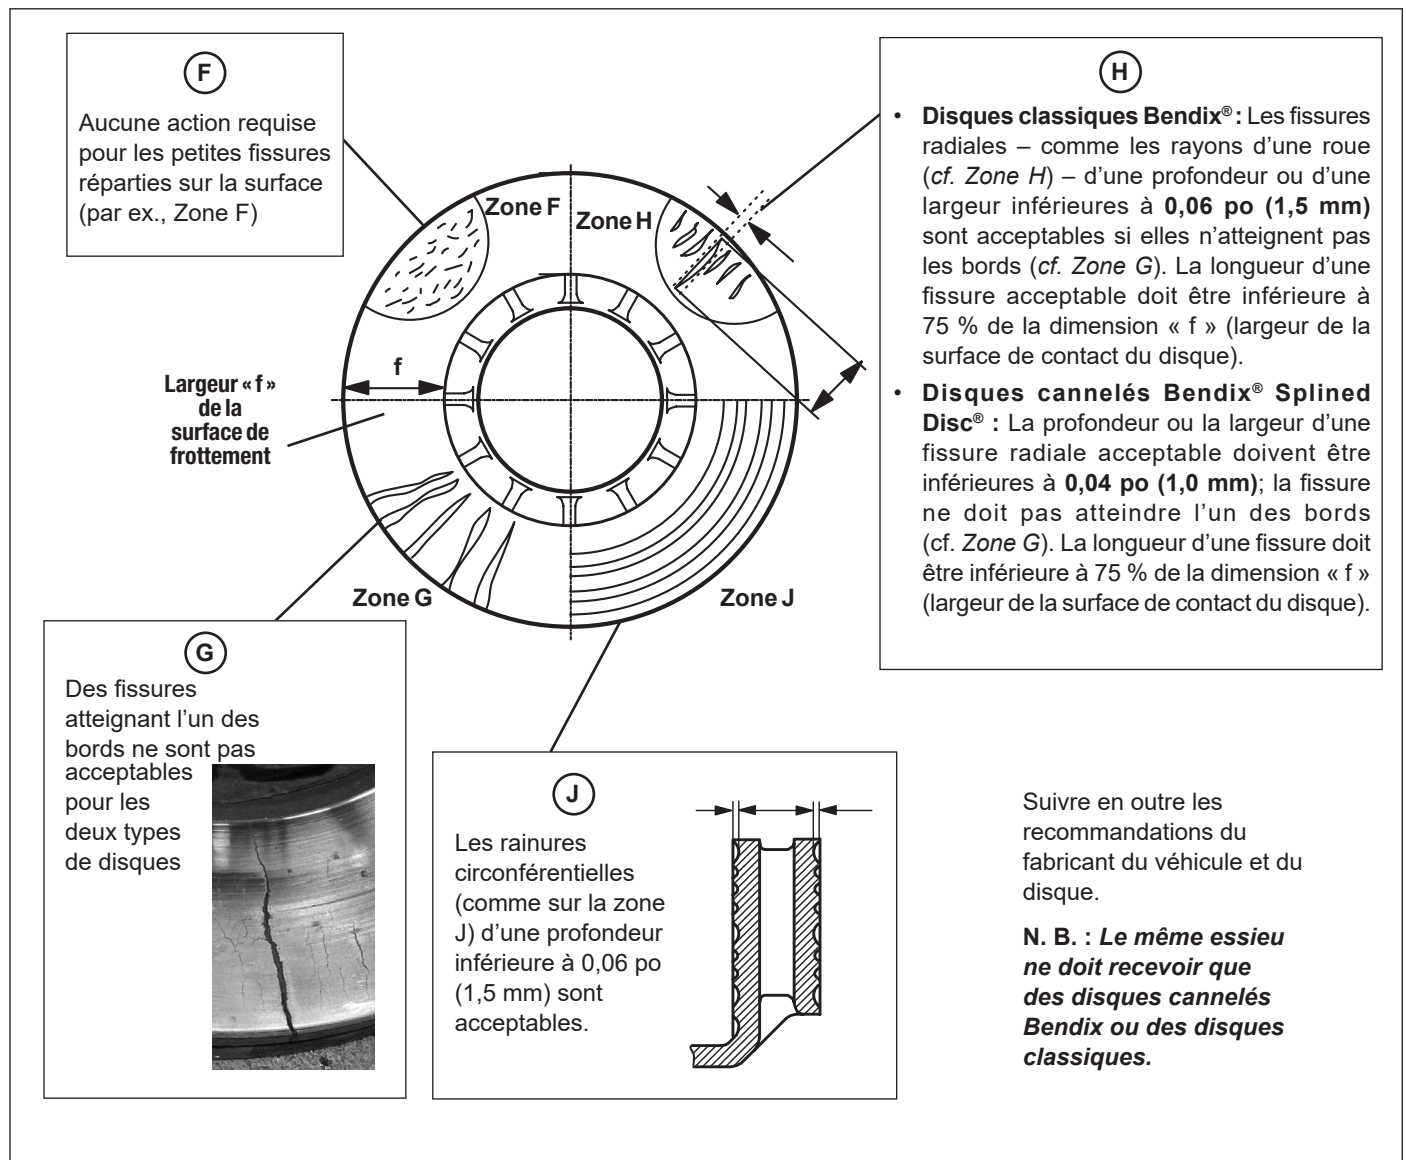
Exemples de conditions du disque acceptables et non acceptables
